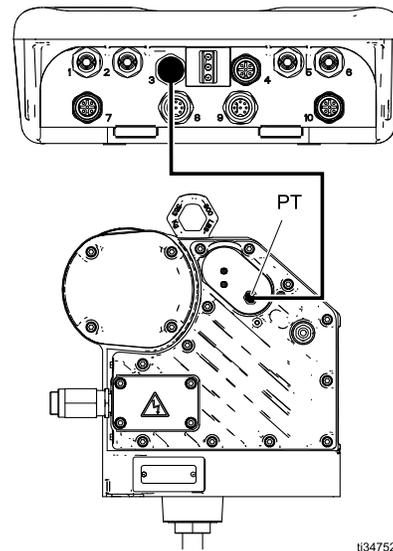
Pumpensteuermodul-Anschlüsse an der E-Flo DC Pumpe, dreiphasig
